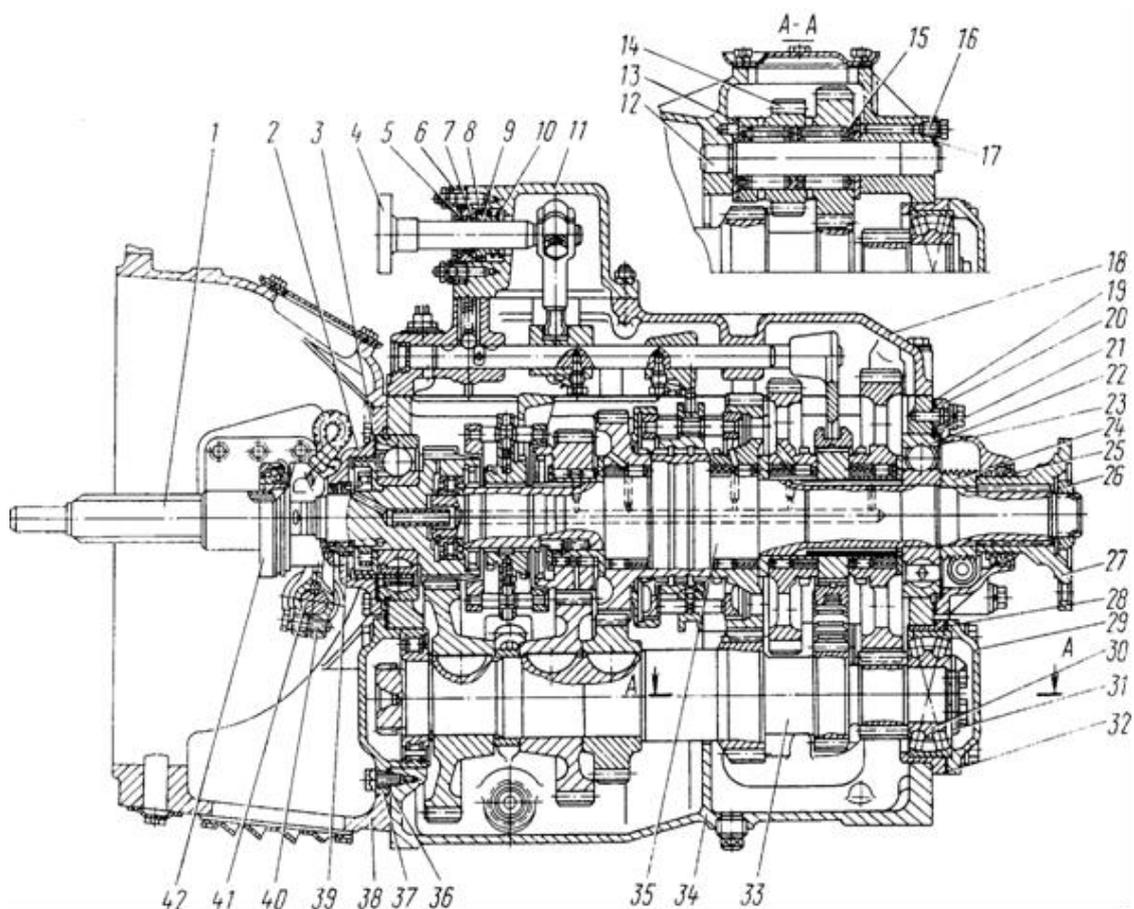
Коробка передач модели 14: 1 – вал ведущий; 2 – крышка заднего подшипника ведущего вала; 3, 23 – прокладки регулировочные; 4 – шток рычага; 5 – кольцо защитное; 6 – крышка опоры рычага; 7 – сухарь опоры рычага; 8 – кольцо уплотнительное; 9 – опора штока; 10 – пружина; 11 – опора рычага переключения передач; 12 – ось блока шестерен заднего хода; 13, 31 – шайбы упорные; 14 – блок шестерен заднего хода; 15 – роликоподшипник; 16 – болт со штифтом; 17 – шайба стопорная; 18 – крышка верхняя; 19, 32, 36 – прокладки уплотнительные; 20 – крышка заднего подшипника ведомого вала; 21 – кольцо стопорное; 22 – шарикоподшипник задний ведомого вала; 24 – червяк привода спидометра; 25, 39 – манжеты уплотнительные; 26 – гайка крепления фланца; 27 – фланец крепления карданного вала; 28 – стакан заднего подшипника промежуточного вала; 29 – крышка подшипника; 30 – роликоподшипник сферический; 33 – вал промежуточный; 34 – картер коробки передач; 35 – вал ведомый; 37 – крышка переднего подшипника промежуточного вала; 38 – картер сцепления; 40 – вилка выключения сцепления; 41 – вал вилки выключения сцепления; 42 – муфта выключения сцепления
